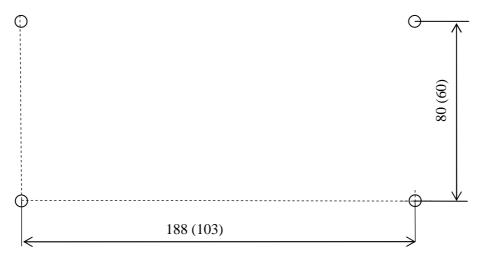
Разметка крепления корпуса УПВК-1У исп.2 и УППВК- значения в скобках.
